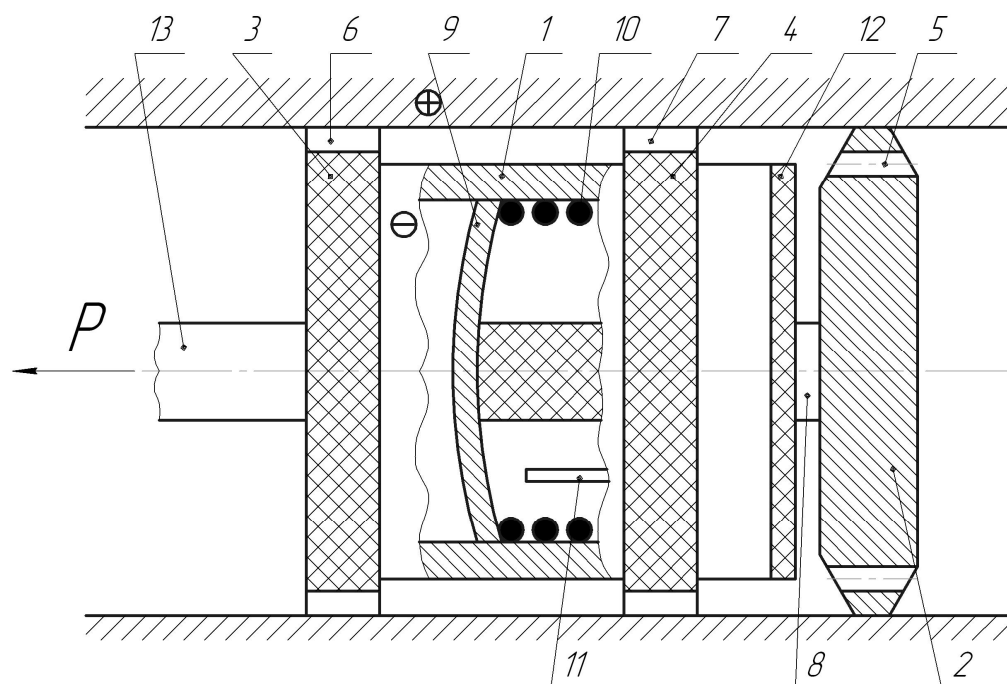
Схема электрохимикомеханической обработки внутренних поверхностей: 1 – рабочая часть (электрод-инструмент); 2 – калибрующий элемент (дорн); 3, 4 – передний и задний направляющие элементы; 5 – отверстия для прохода электролита; 6, 7 – пазы для прохода электролита; 8 – тяга; 9 – диафрагма; 10 – упругий элемент; 11 – шток прерывателя тока механизма для протягивания; 12 – диэлектрическая прокладка; 13 – токоподвод
